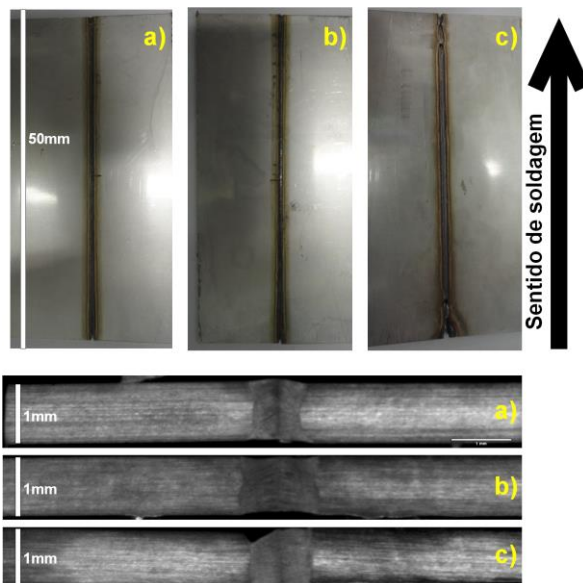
Amostras de soldagem LASER autógena (Autor)
